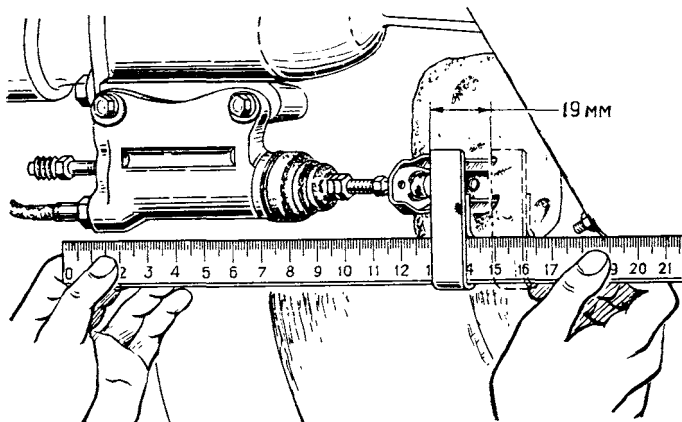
Замер хода толкателя рабочего цилиндра сцепления
